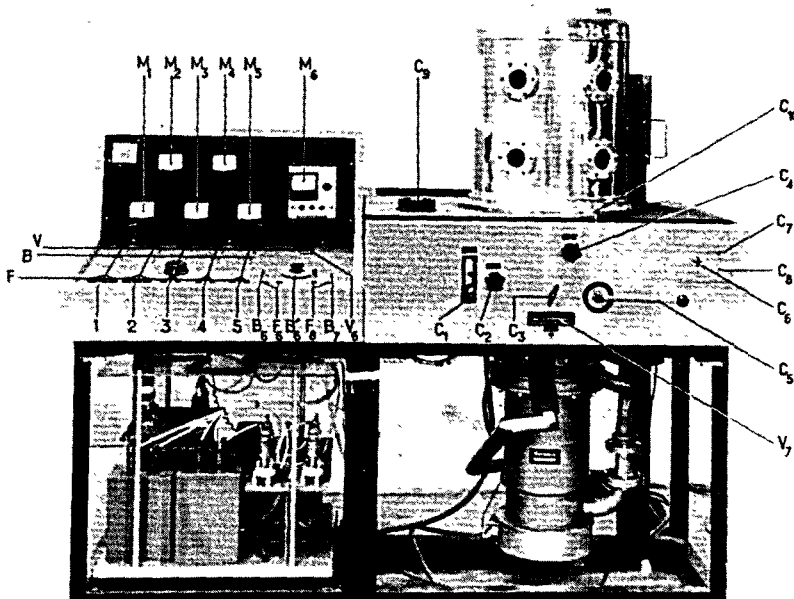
Elektronenstrahl-Schweißmaschine der Firma Sciaky
